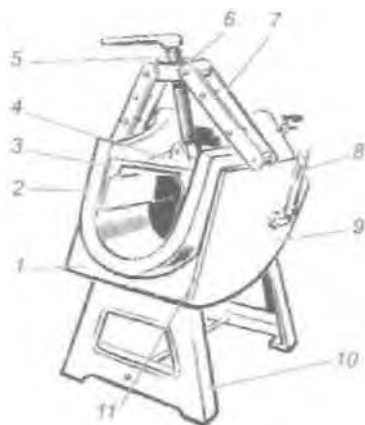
Секторная форма-мульда: 1 — корпус; 2 — паровая рубашка; 3 — бортовые вкладыши; 4 — подпятник; 5 — нажимный винт; 6 — траверса струбцины; 7 — струбцина; 8 — термометр; 9 — щиток; 10 — чугунная подставка; 11 — асбест для теплоизоляции корпуса мульды поверхности шины. В ее верхней части имеется прижимное устройство — струбцина 7.
